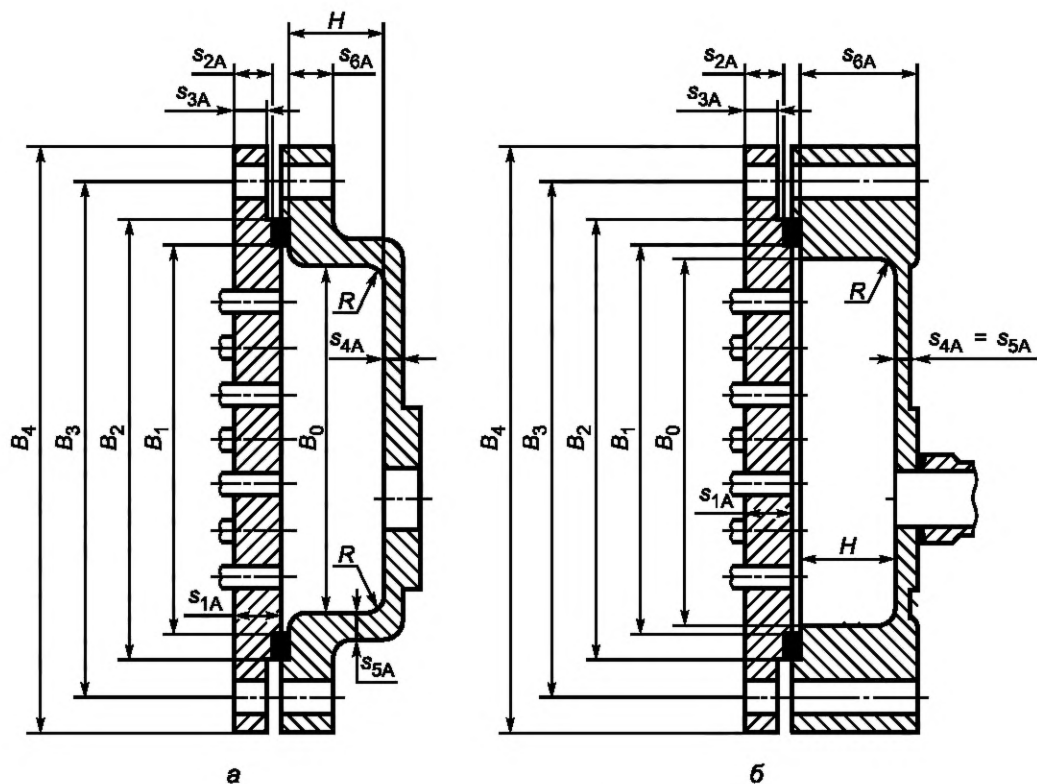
Камера разъемной конструкции с литой крышкой
